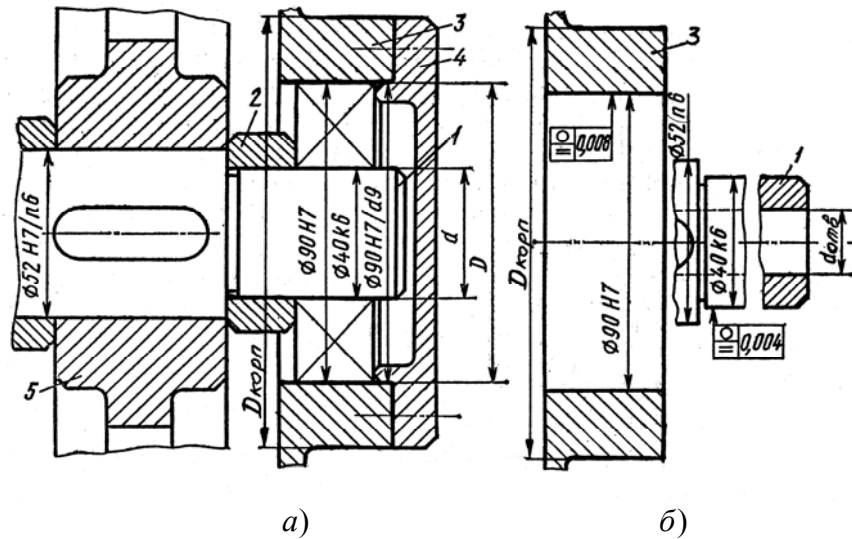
Обозначение посадок подшипников качения на сборочных чертежах (а) и полей допусков на чертежах деталей (б):
